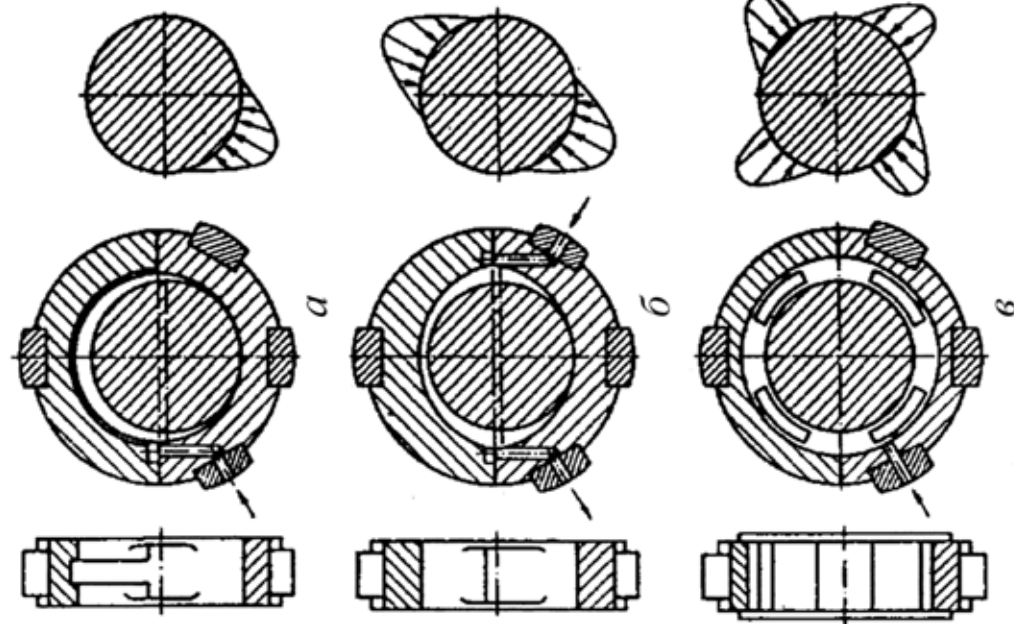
Варианты расточки опорных подшипников: *a* – одноклиновые вкладыши с цилиндрической расточкой; *б* – двухклиновая-лимонная (эллиптическая) расточка; *в* – сегментные подшипники
